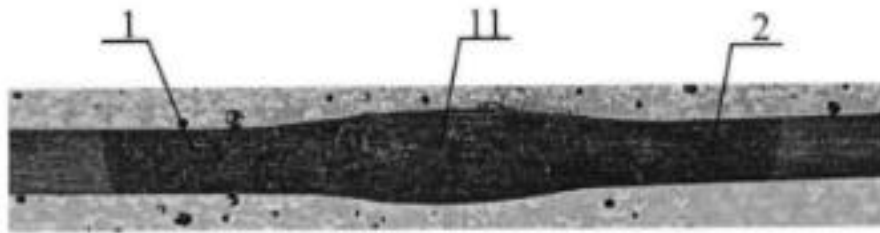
поперечний переріз зварного шва деталей товщиною 1,5 мм.
